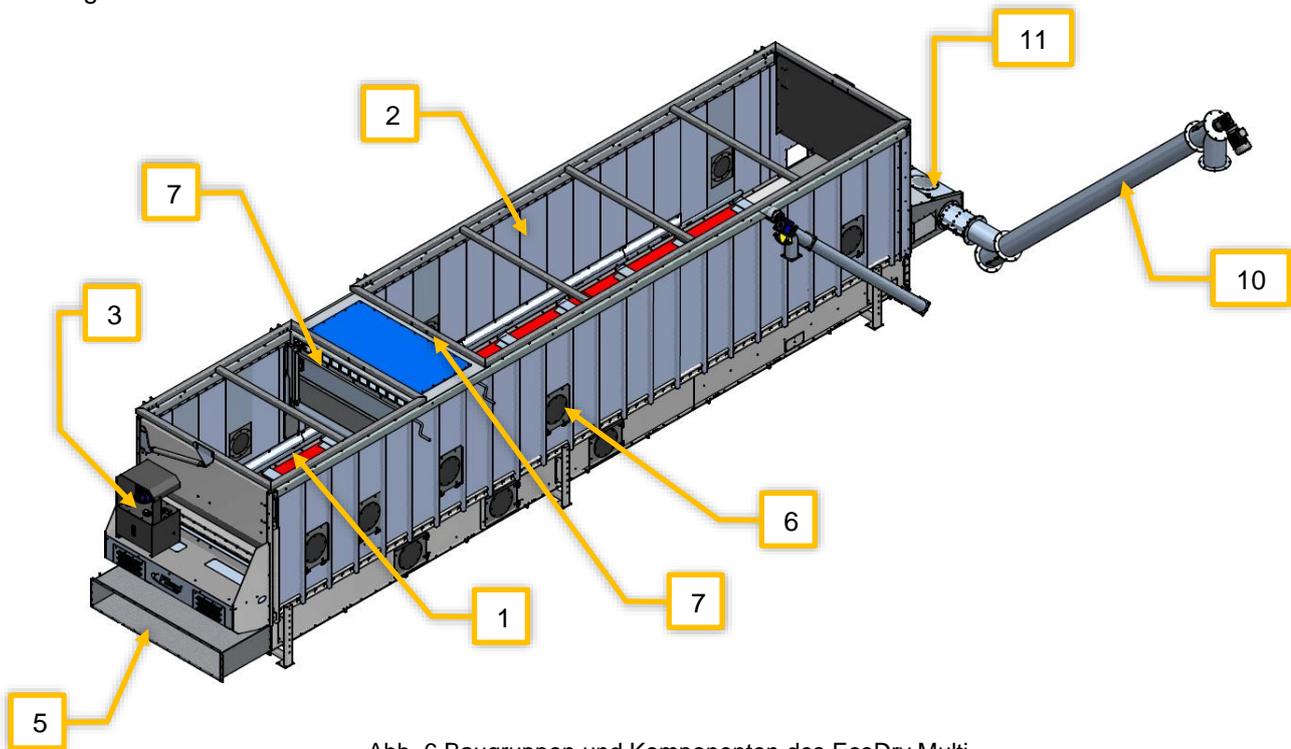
Baugruppen und Komponenten des EcoDry Multi
